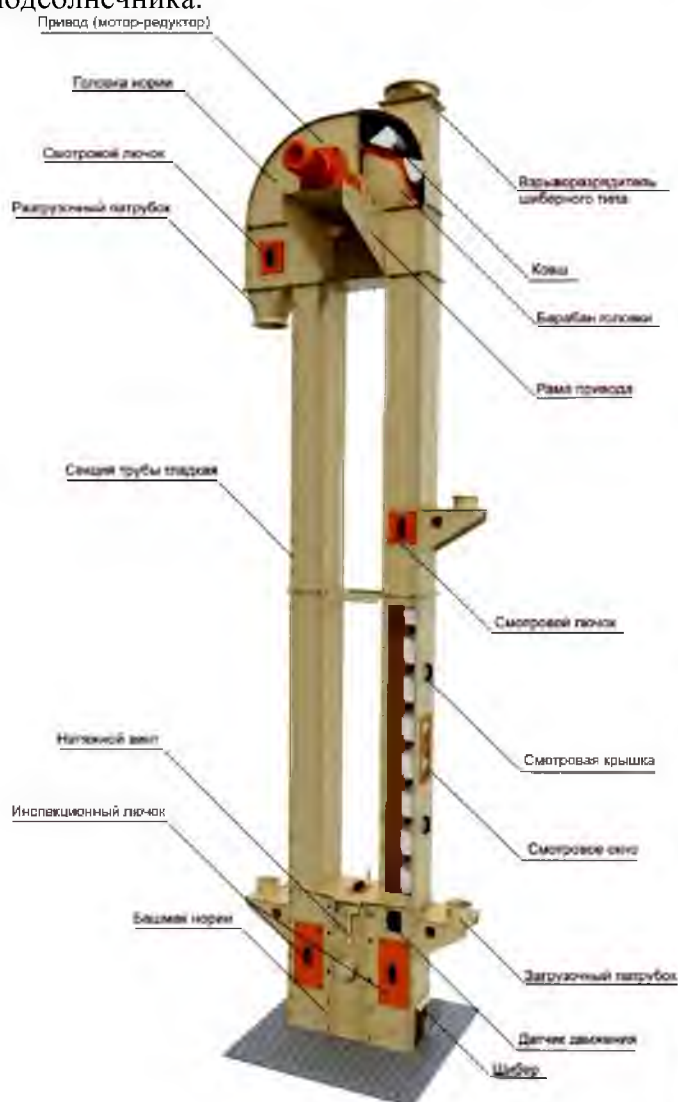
конструкция нории типа НЦ и вид ковша
